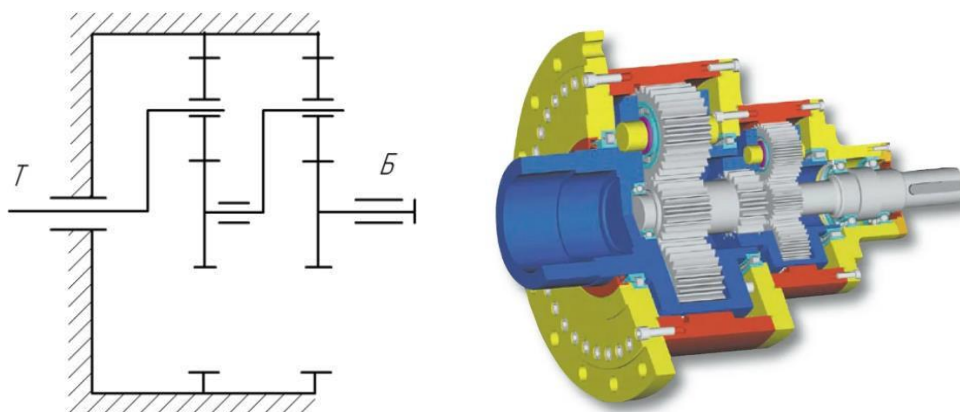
Двухступенчатый планетарный редуктор
